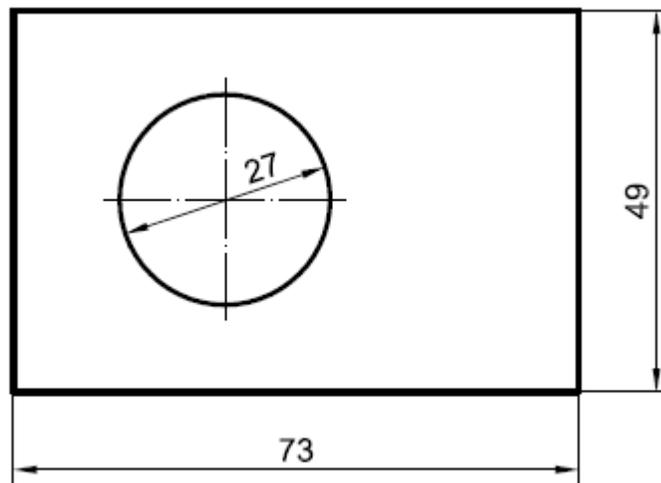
Cotas de dimensión en una vista de una pieza.
